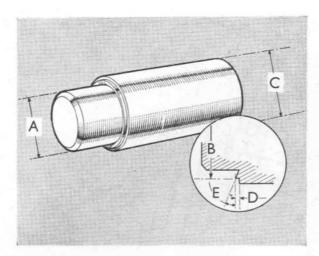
OUTIL D'EMMANCHEMENT DU ROULEMENT A AIGUILLES
